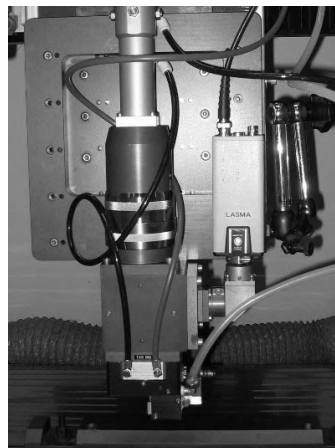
Verwendeter Schweißkopf für die Versuche mit dem Scheibenlaser
